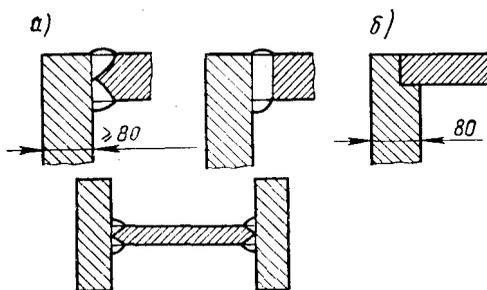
Сварные соединения станин прессов, выполненных из толстолистового проката
